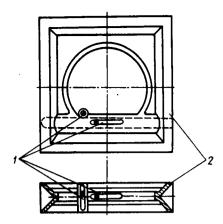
Монтажно-ремонтный уровень: — ампула; 2 — корпус
